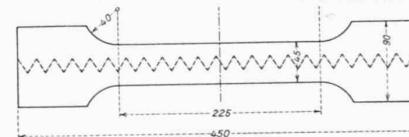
Zerreissprobstab mit Schweißnaht in der Stabaxe.
